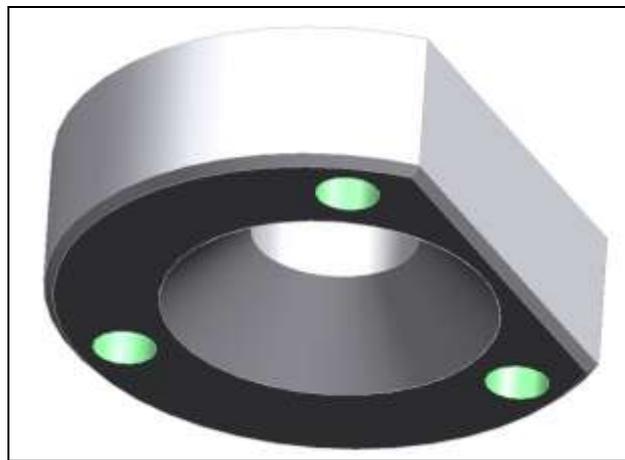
Flangia cilindrica di centraggio, parte superiore
